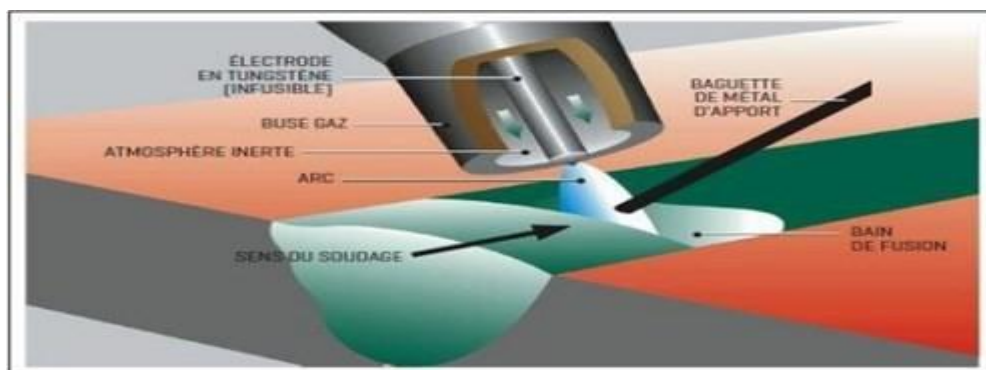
Soudage TIG (Tungstène Inerte Gaz) [7].
